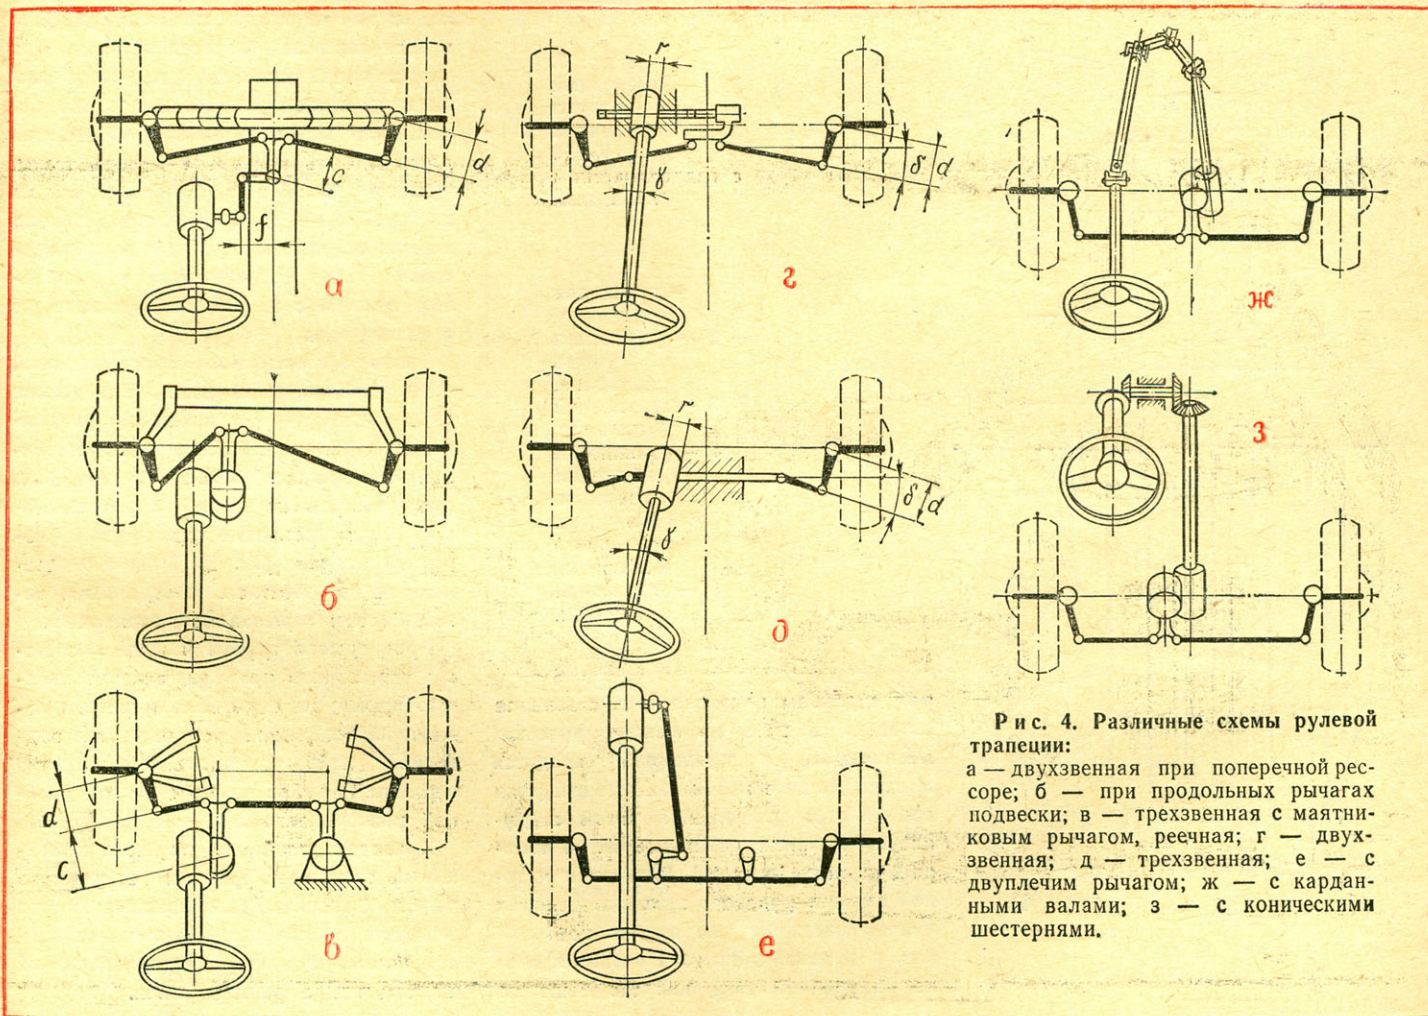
Различные схемы рулевой трапеции: а — двухзвенная при поперечной рессоре; б — при продольных рычагах подвески; в — трехзвенная с маятниковым рычагом, реечная; г — двухзвенная; д — трехзвенная; е — с двуплечим рычагом; ж — с карданными валами; з — с коническими шестернями.
